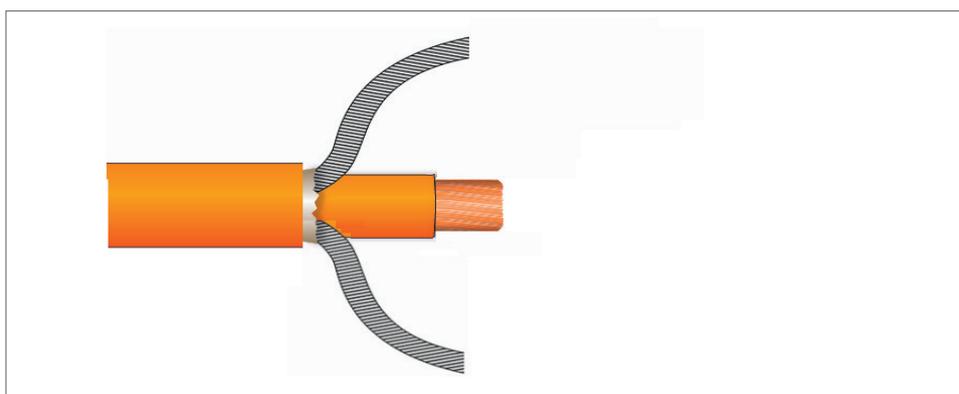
Schritt 4 (HV BM 1.2+S): Innenmantel entfernen
